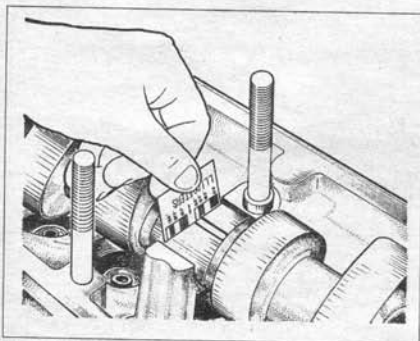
Измерение зазора между шейками распределительного вала и корпусами подшипников
